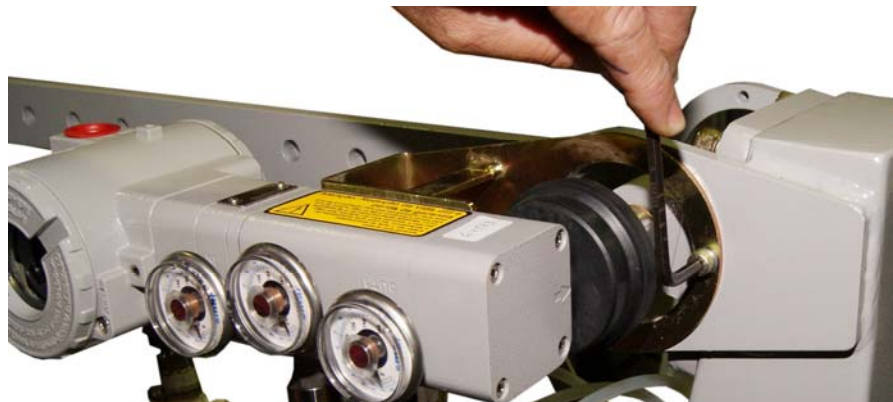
Montagem do Conjunto "posicionador + suporte" na Base
